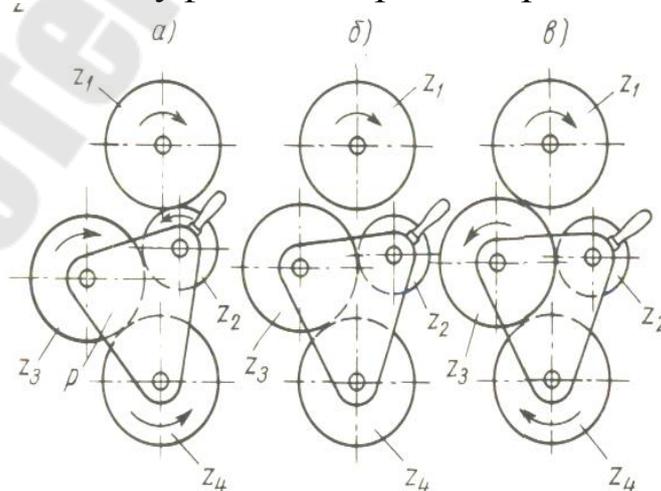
Схема реверса с двумя паразитными колёсами
